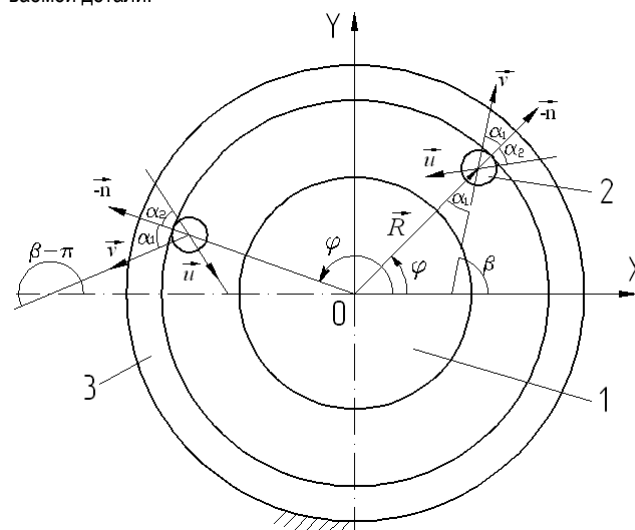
Схема соударения деформирующего шара с обрабатываемой поверхностью детали (1 – магнитный ротор инструмента, 2 – деформирующий шар, 3 – обрабатываемая деталь)
